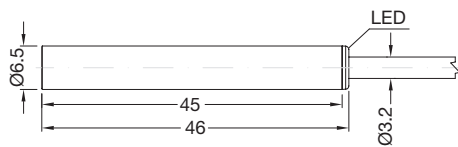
Lange Ausführung, bündiger Einbau, Kabel
